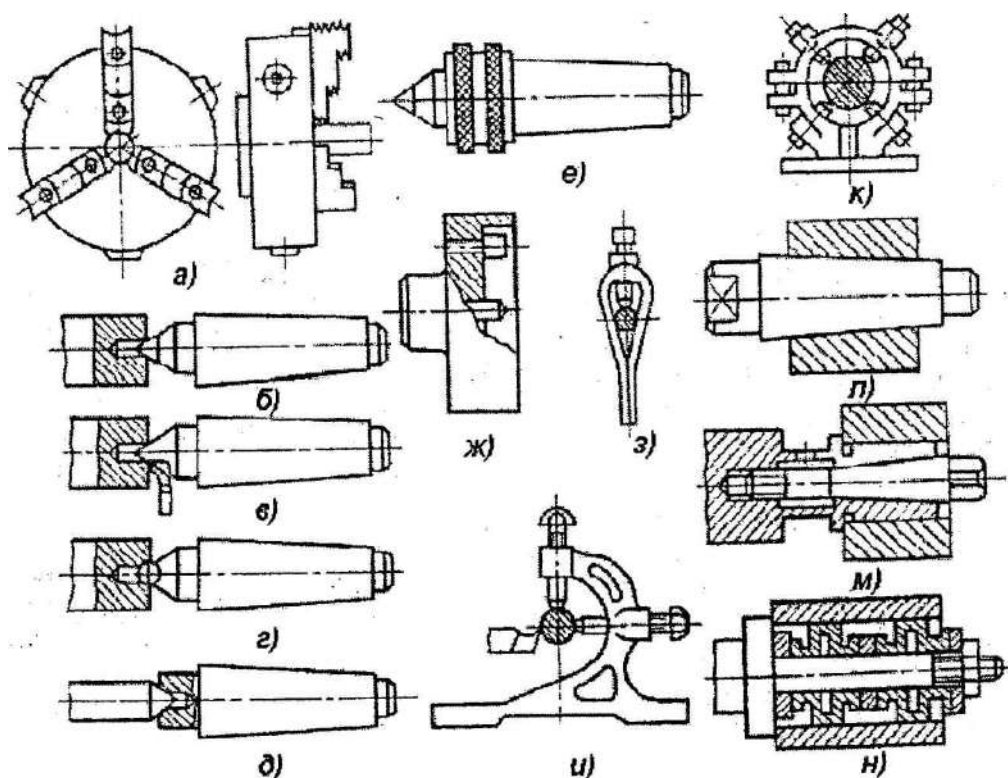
Приспособления для закрепления заготовок на токарных станках
